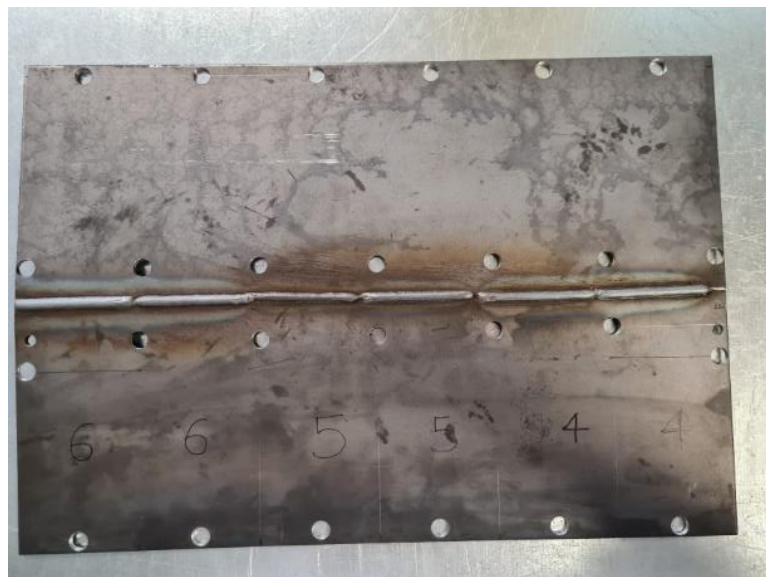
Chapa soldada de acordo com os experimentos 4, 5 e 6 da matriz ortogonal de Taguchi.
